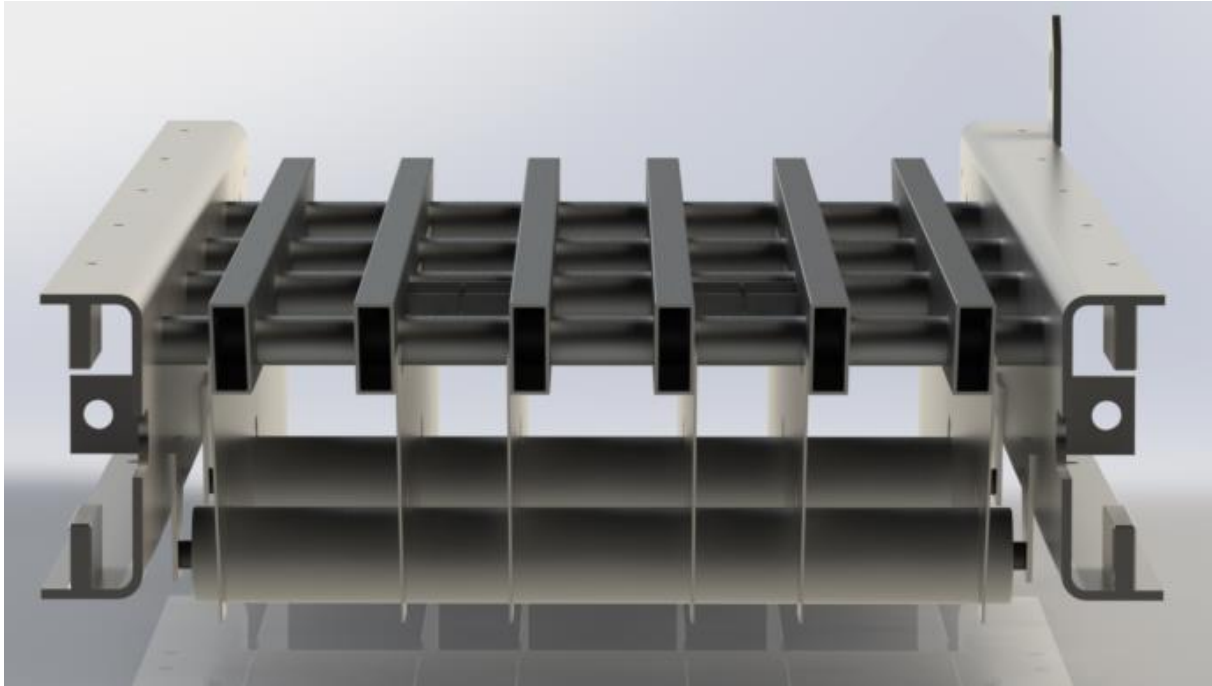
Disposición de chapas cubre cadena y rodillos de retorno
